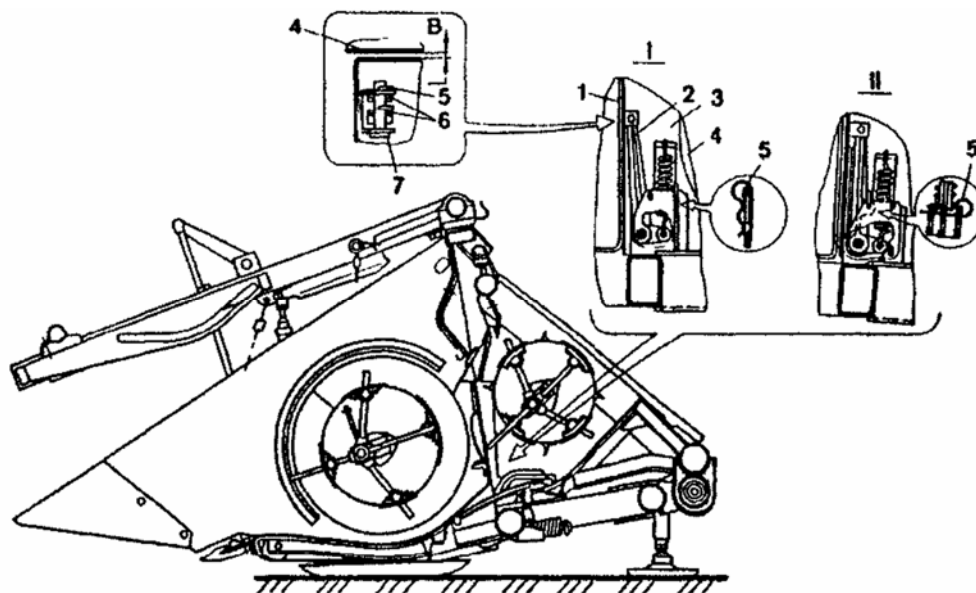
Жатка с боковым уплотнительным щитком:
